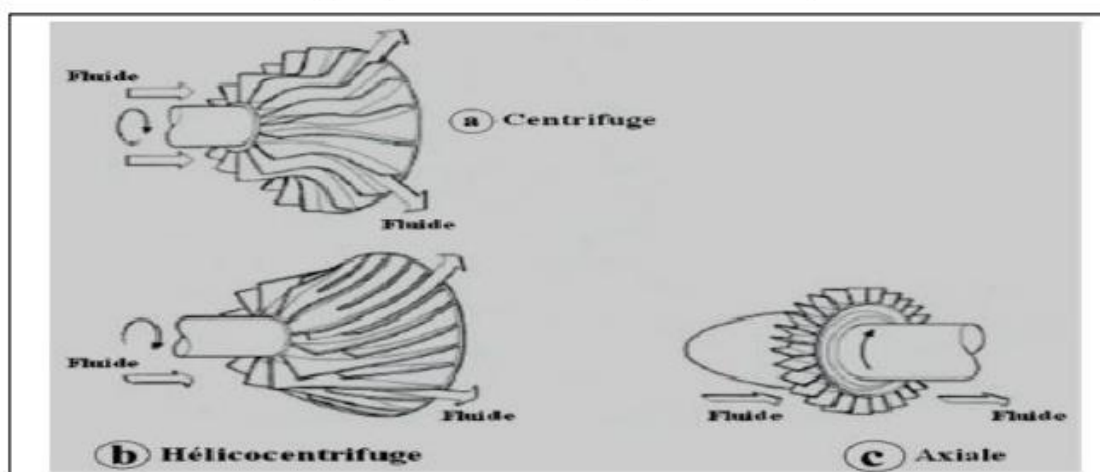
Roues mobiles de machines centrifuge, hélico centrifuge et axiale
